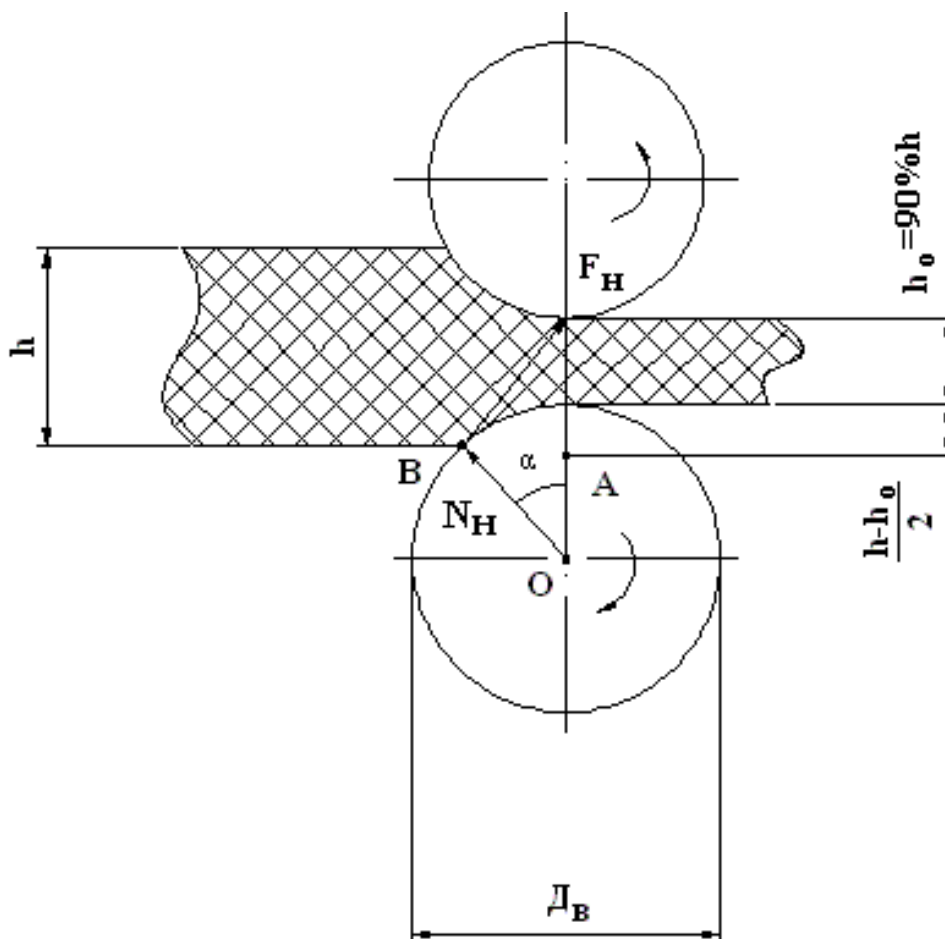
Схема захоплення рифленими вальцями деталі
